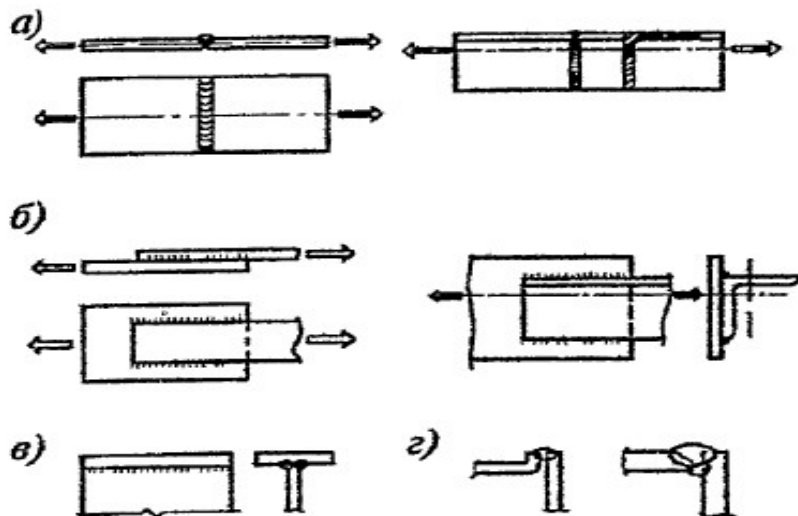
Типы сварных соединений: стыковыми швами - а) – листов и уголков; угловыми швами - б) – нахлесточное, в) – в тавр, г) – в угол.
